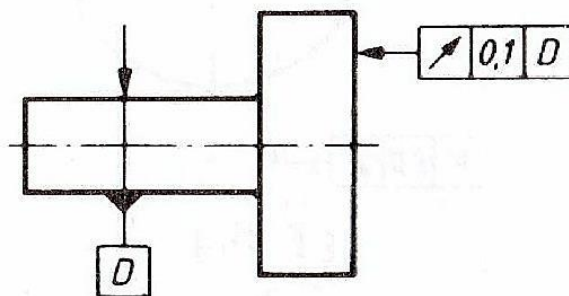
Axial run-out, indicazioni a disegno: D è l'asse di riferimento [35]
